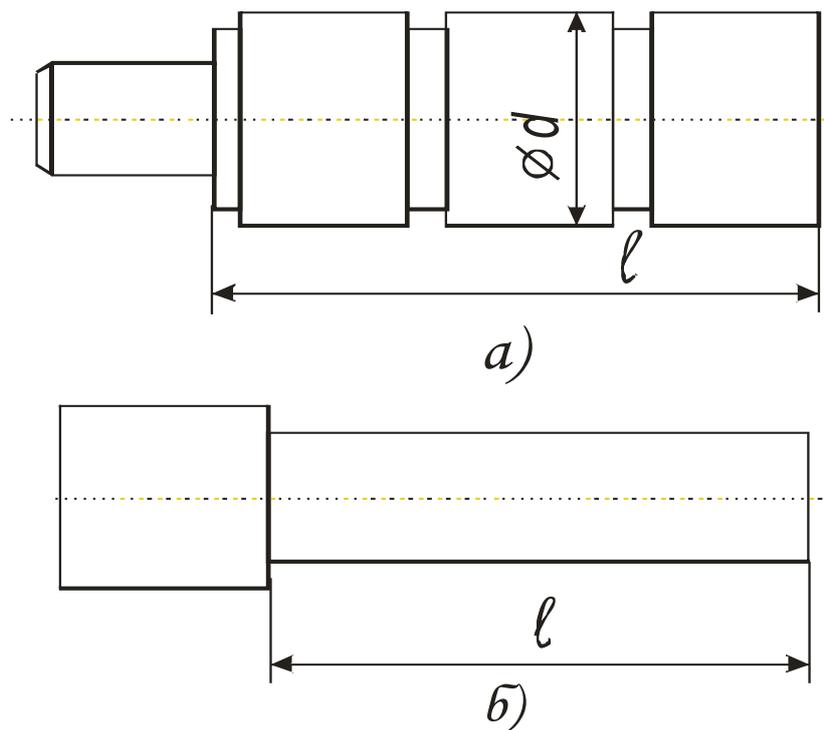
Жесткая (а) и нежесткая (б) заготовки
